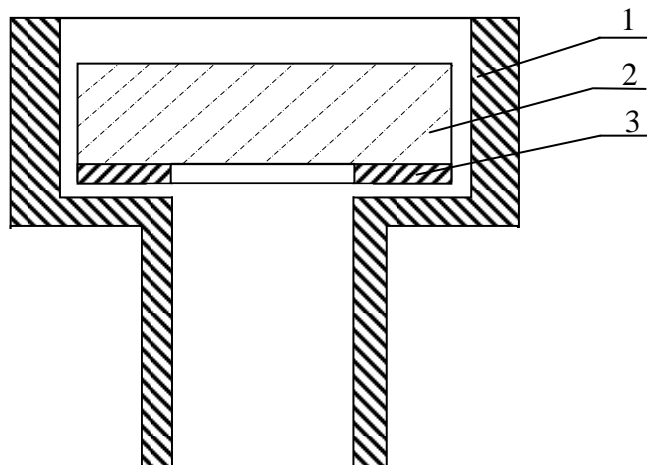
Стандартная конструкция паяного окна в металлический корпус: 1 — чашка металлического корпуса; 2 — окно; 3 — припой
